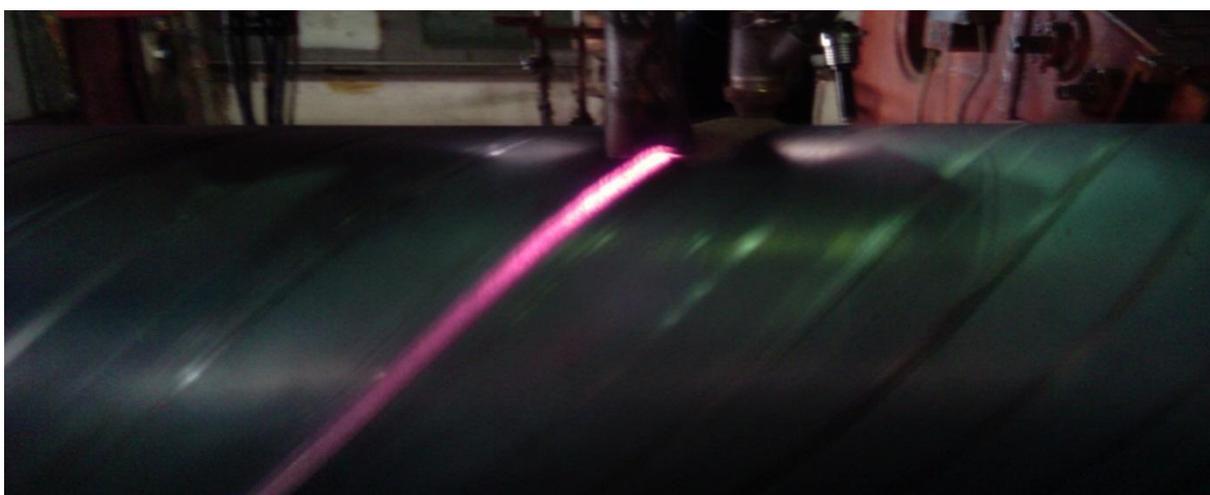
Tube préparé à la machine à souder en spirale
